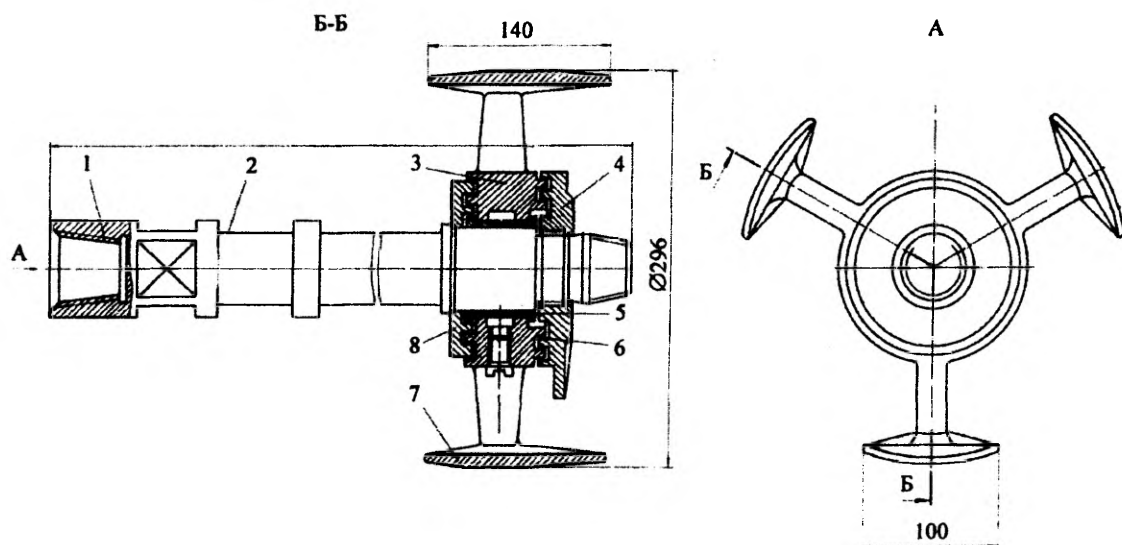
Опорный фонарь бурового станка БГА-4М
